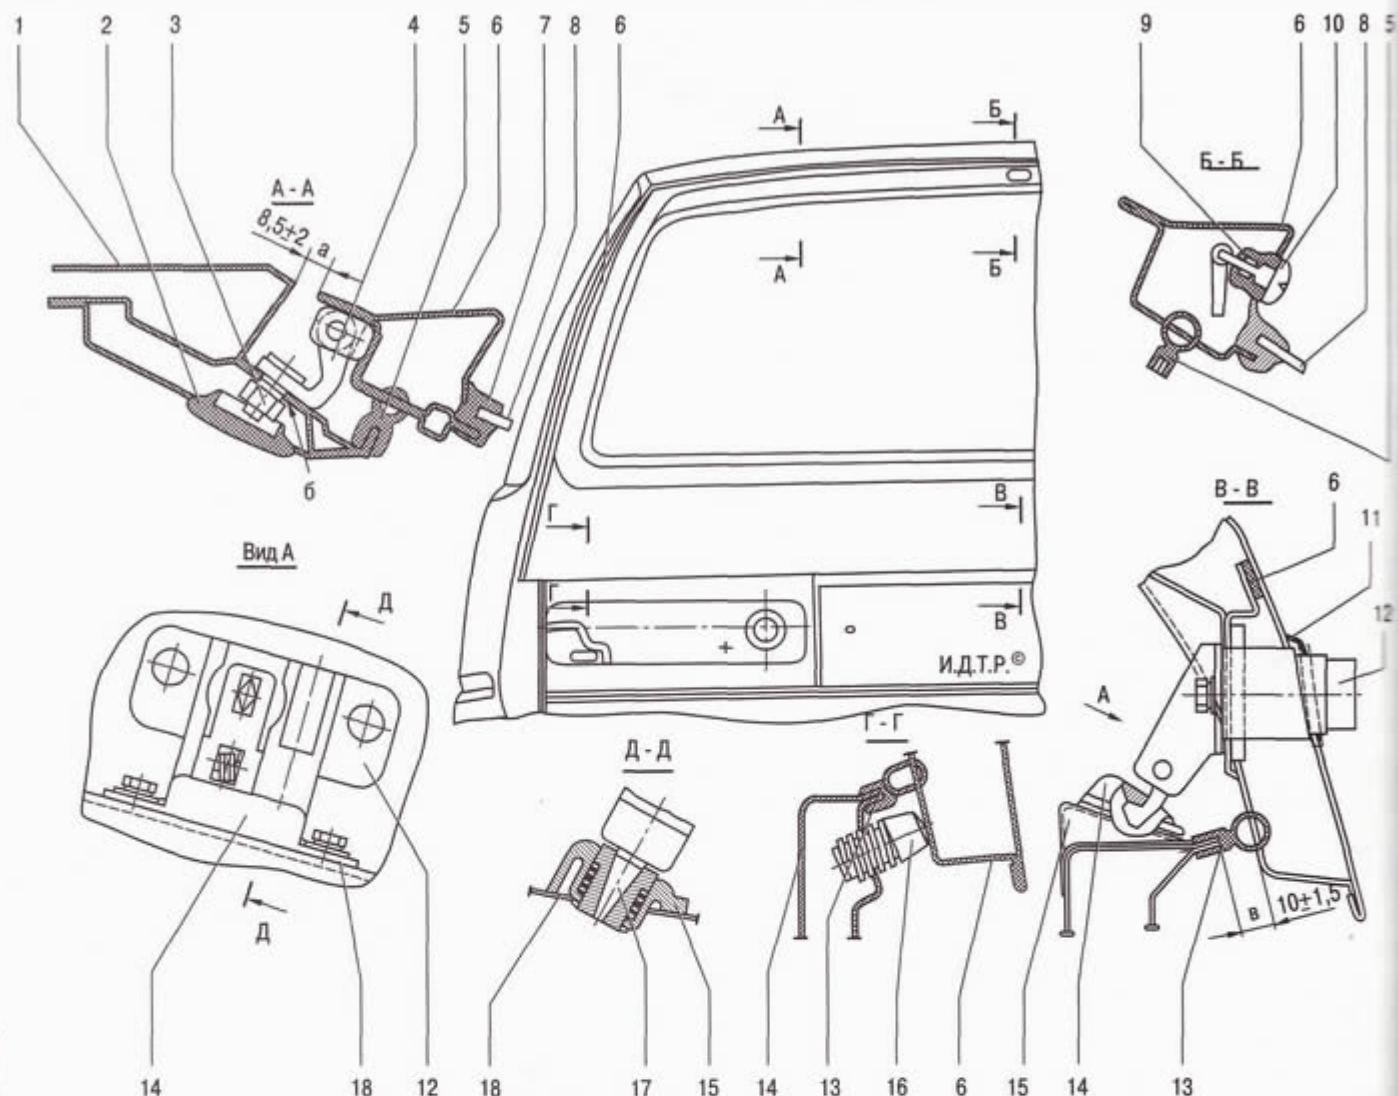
Дверь задка и ее арматура: а – зазор между дверью и крышей; б – увеличенные отверстия в кузове для крепления петли; в – зазор между дверью и торцами панели задка; 1 – кузов; 2 – заглушка; 3 – гайка крепления петли; 4 – петля; 5 – боковой уплотнитель; 6 – дверь задка; 7 – уплотнитель стекла; 8 – стекло двери задка; 9 – уплотнитель жиклера; 10 – жиклер; 11 – прокладка замка; 12 – замок двери задка; 13 – нижний уплотнитель; 14 – фиксатор двери задка; 15 – панель кузова; 16 – ограничитель двери; 17 – шип замка; 18 – регулировочная прокладка
